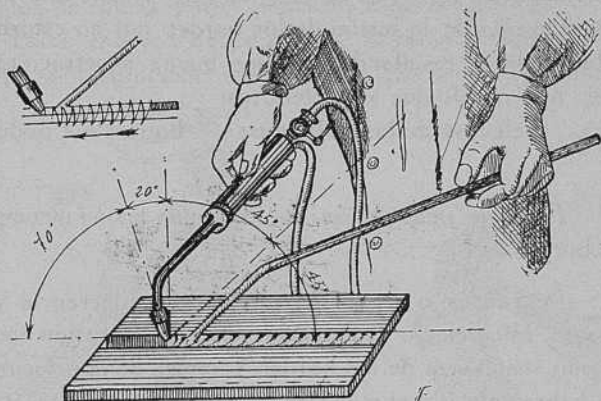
Posición para la soldadura hacia atrás.
